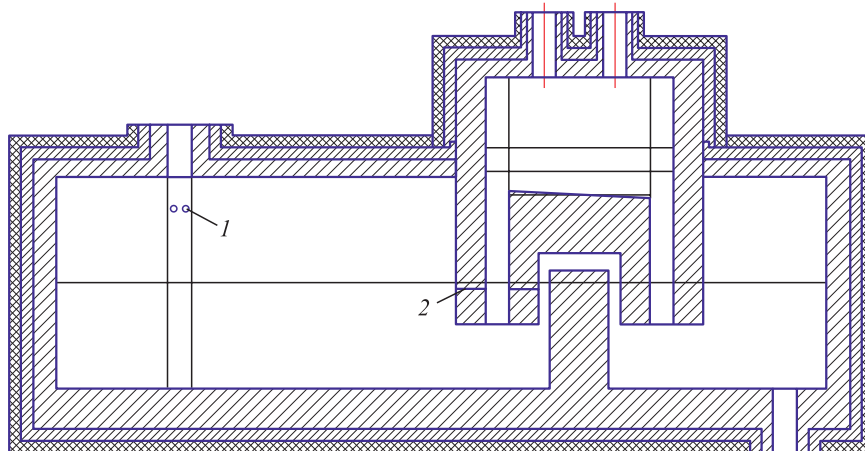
Эскизный чертеж агрегата внепечной обработки расплава
